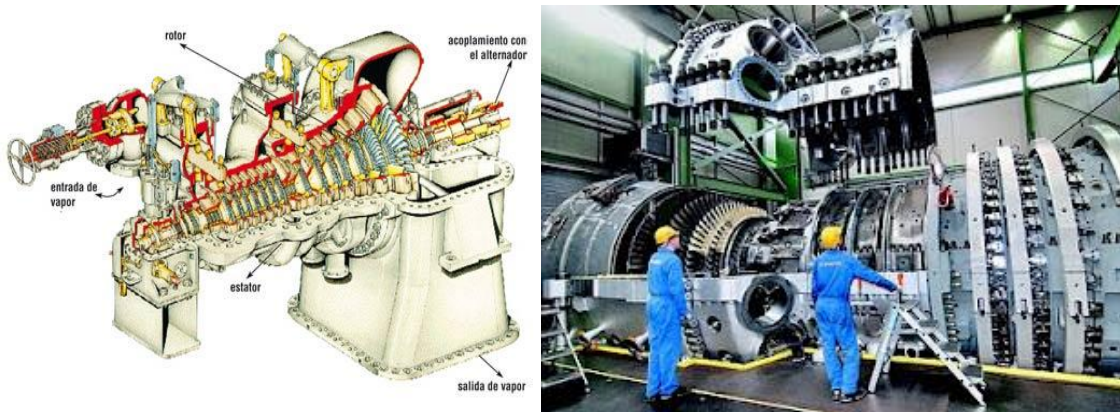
A la izda. Principales partes de una turbina de vapor, a la dcha. Turbina de vapor de la planta Solar Tres, fabricada por Siemens.
